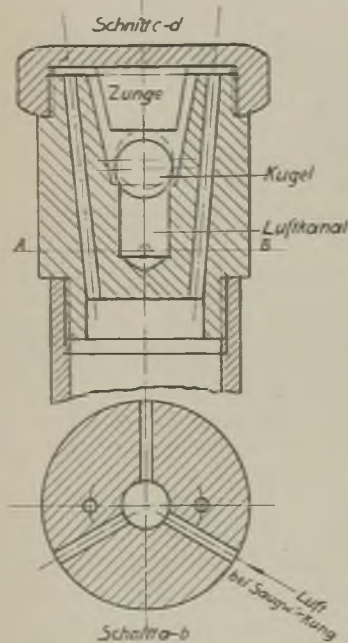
Belüftungsventil für eine Hauswasserleitung.
